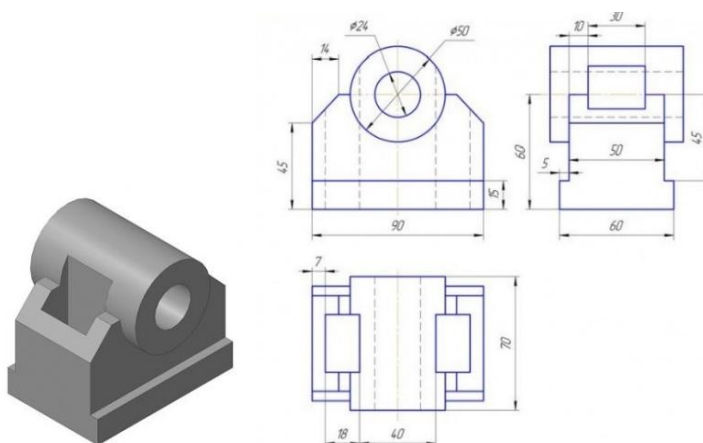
3D-модель детали и комплексный чертеж детали
